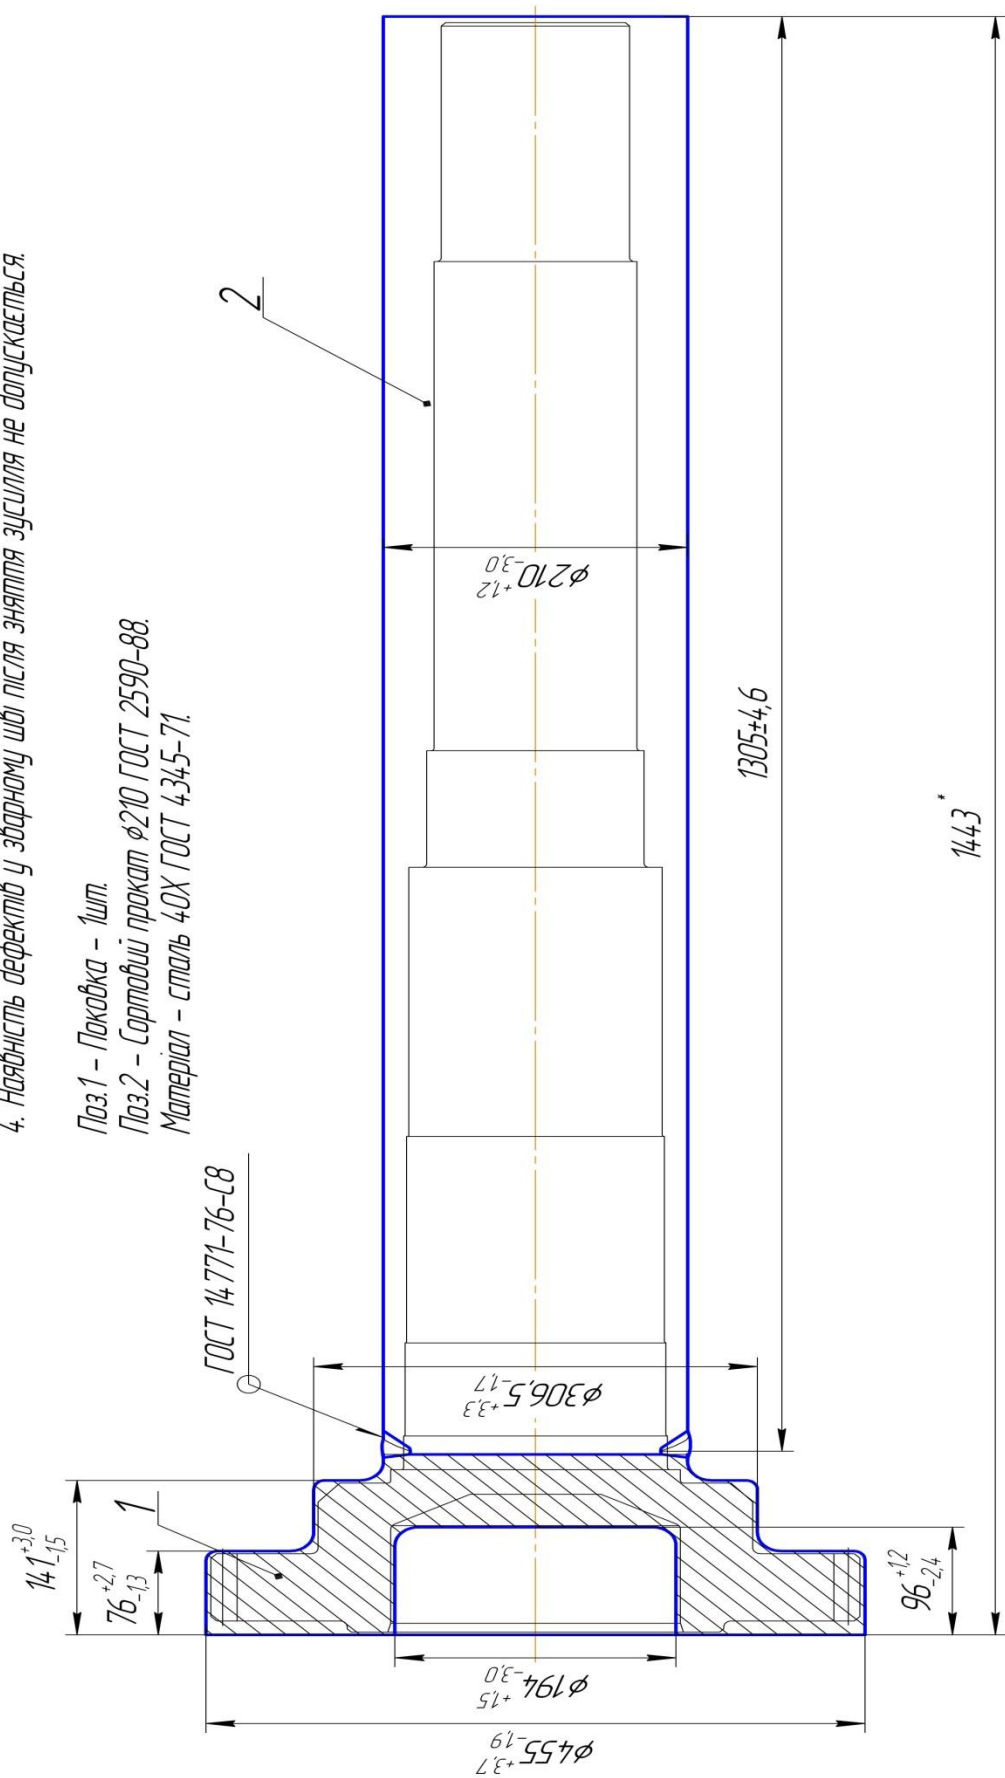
Креслення зварної заготовки деталі вал
